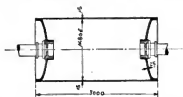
Trommel für einen Trockenapparat, allseitig geschweißt, abgedreht und poliert.
